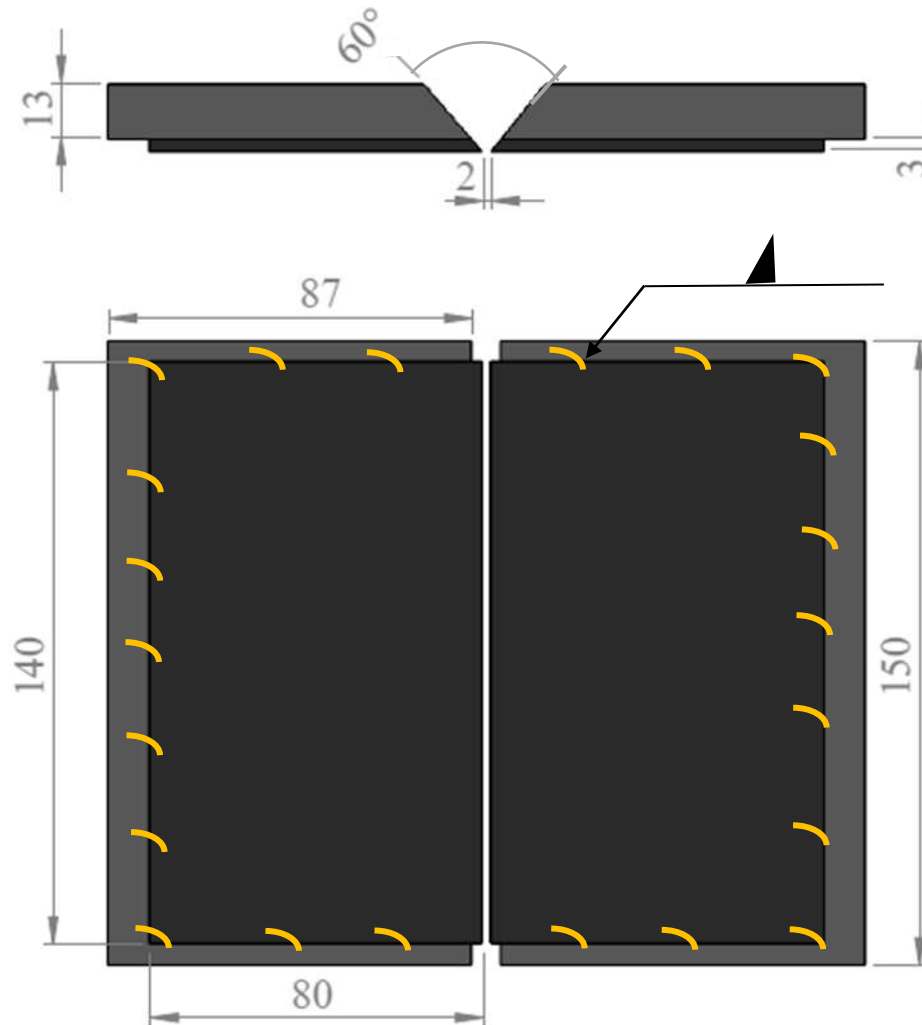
Vista frontal e inferior de la preparación de la junta para las soldaduras A y B (cotas en mm).
